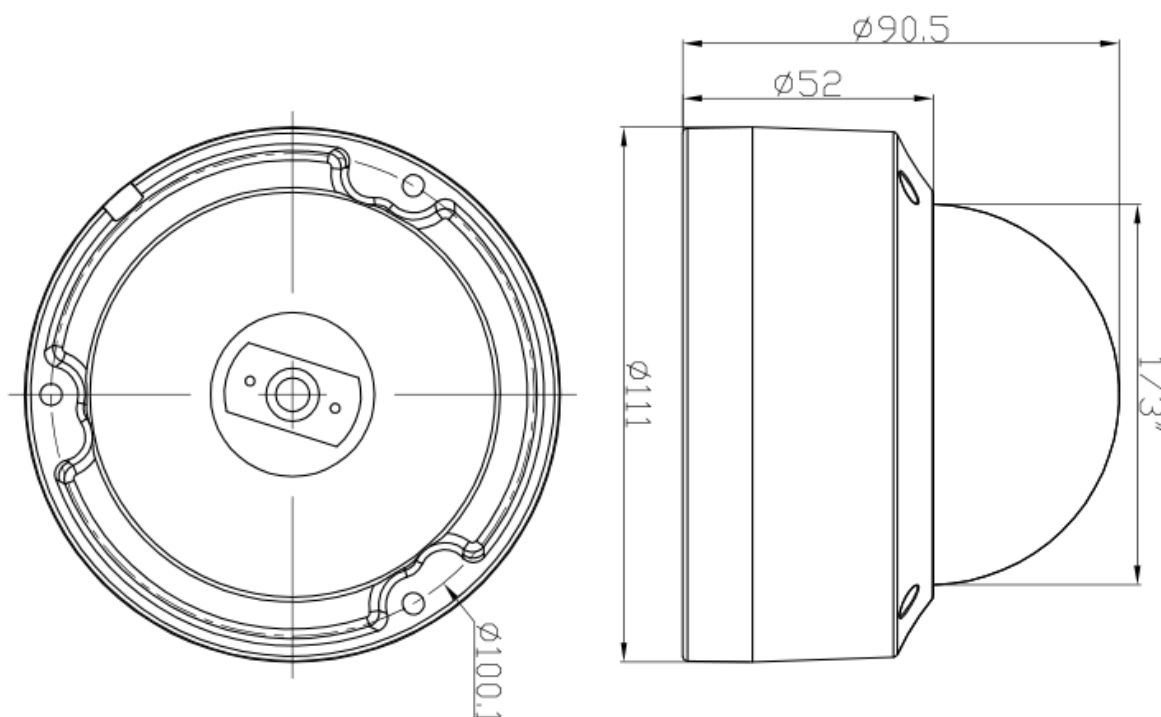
Габаритный чертеж видеокамеры ИВМС-401.
